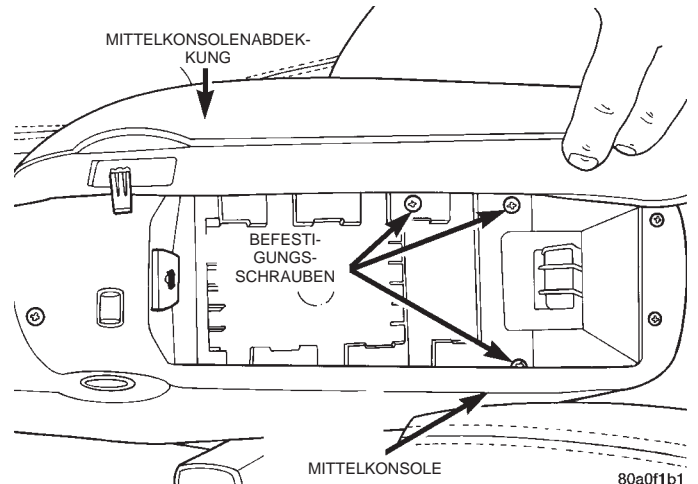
Hintere Befestigungsschrauben der Mittelkonsole
